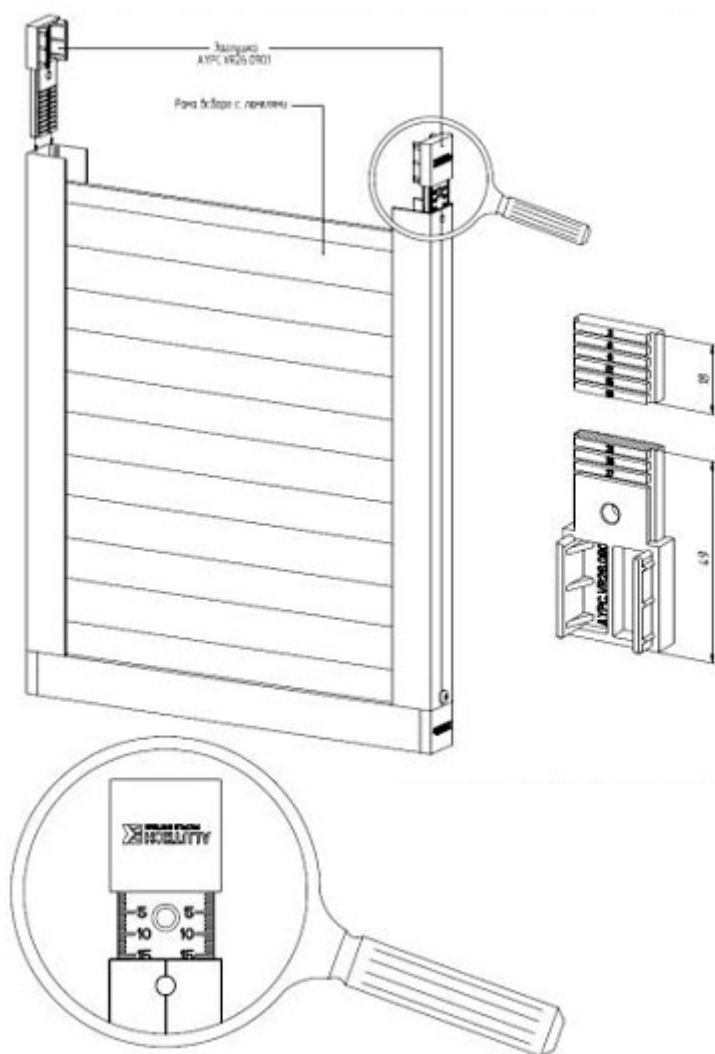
Обработка и установка заглушки АУРС.VR26.0901
